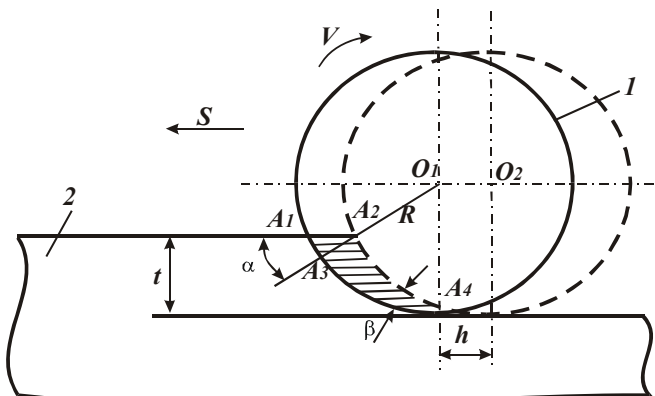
Расчетная схема цилиндрического фрезерования: 1 – фреза; 2 – обрабатываемый материал.
